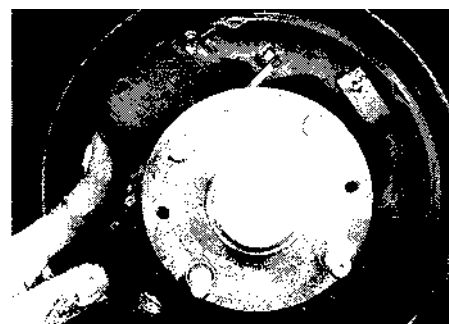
,с. Утопите передний поршень колесного тормозного цилиндра и...
